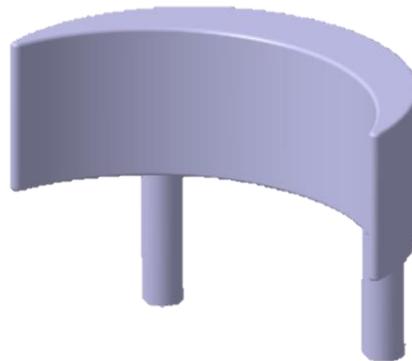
Diseño final respaldo silla. Fuente: CATIA
